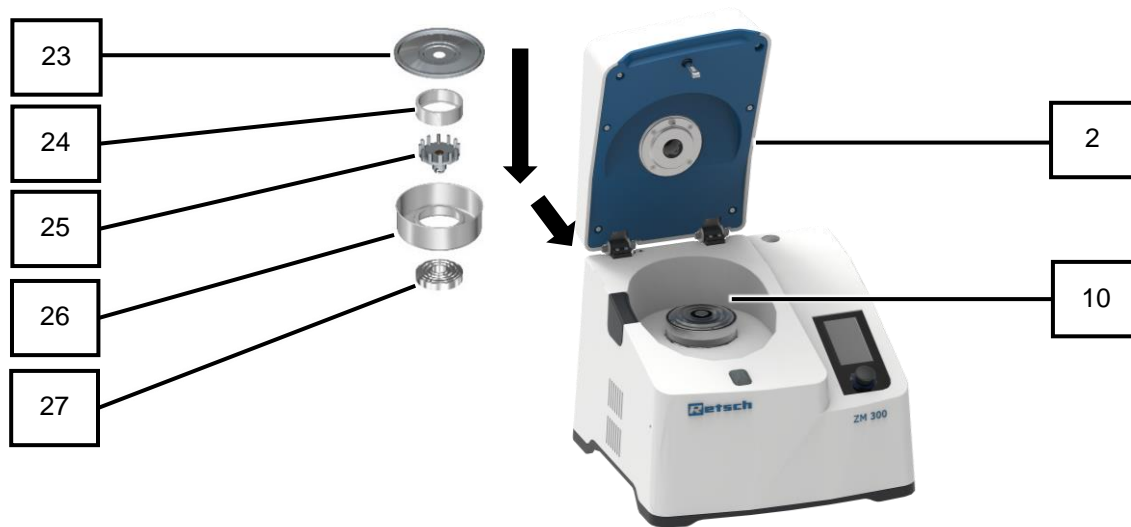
Übersicht Mahlwerkzeuge und Kassette
